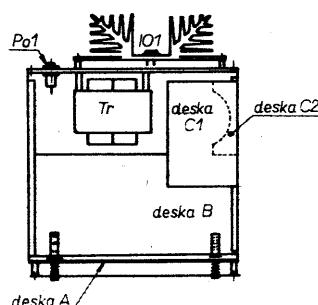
Laboratorní zdroj – pohled ze spodní strany
